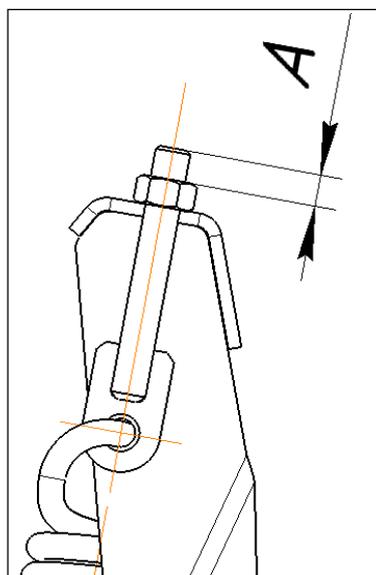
Размер «А» выхода резьбовой части натяжителя без предварительного натяжения пружин подвески
